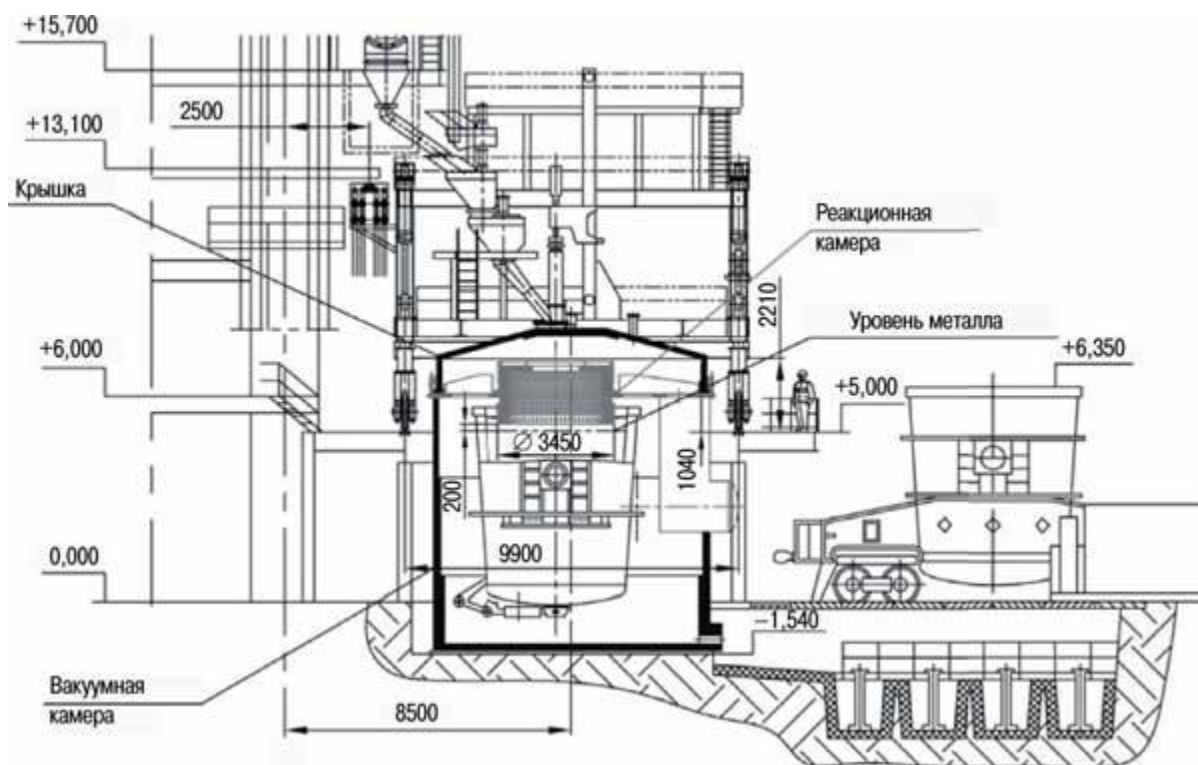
Схема установки камерного вакуумирования конвертерной стали в сталеразливочном ковше
